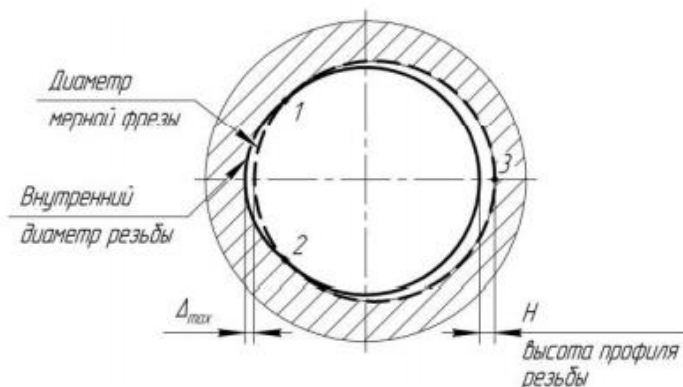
Схематический профиль резьбы в осевом сечении детали
